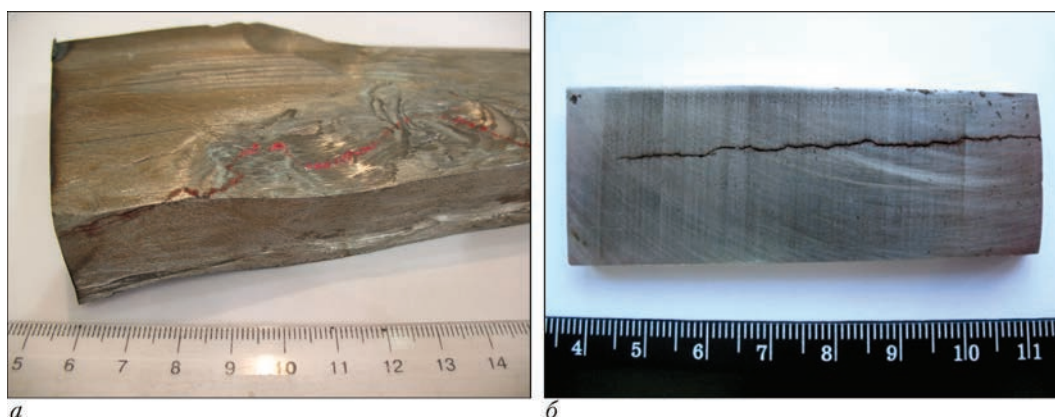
Трещины в сварном соединении (капиллярный контроль): а – с внутренней стороны сварного шва; б – на поверхности темплета
